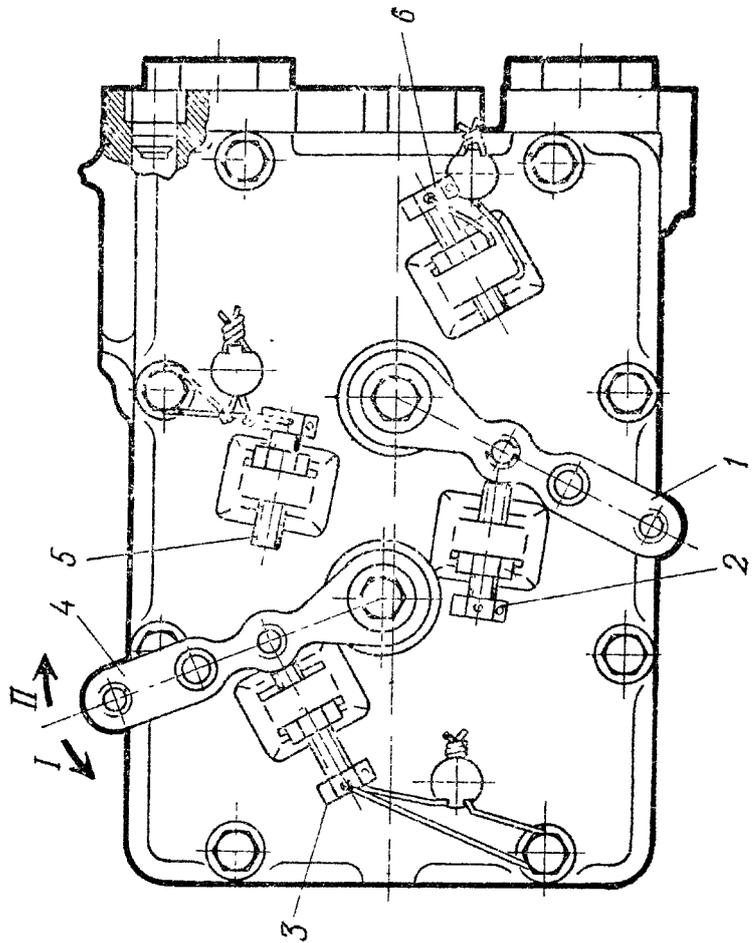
Крышка регулятора с рычагами подачи топлива и останова двигателя:
